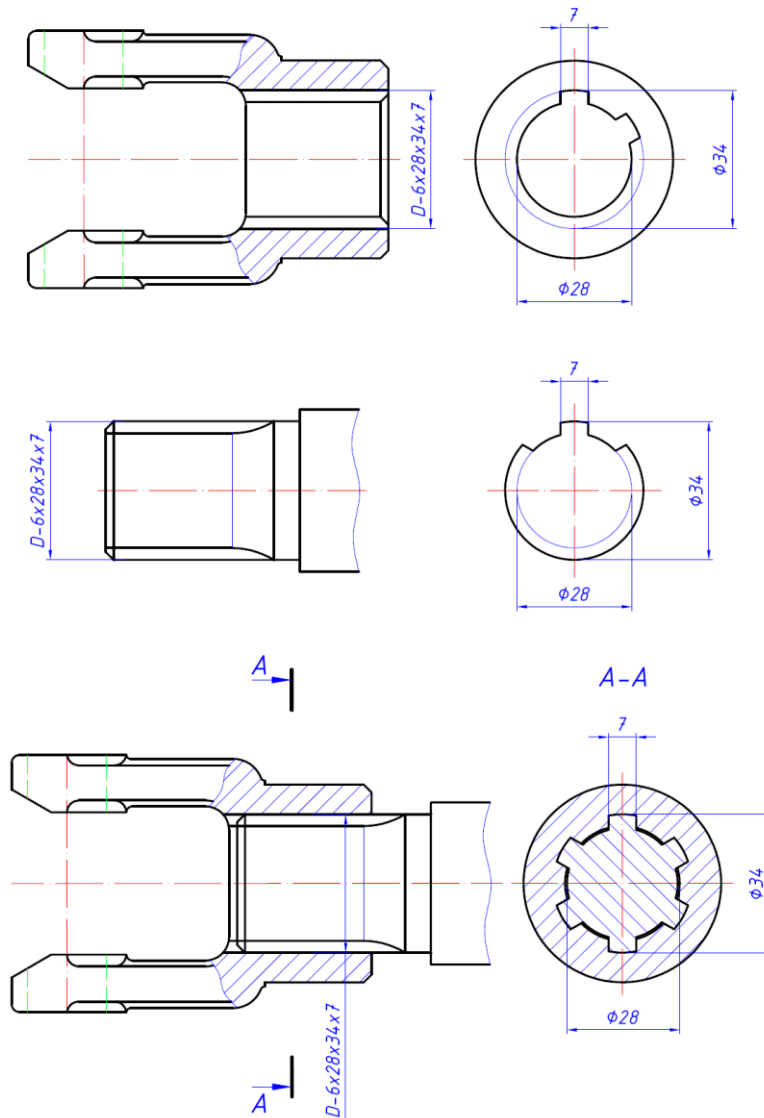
Обозначение на чертеже прямобочного шлицевого соединения
